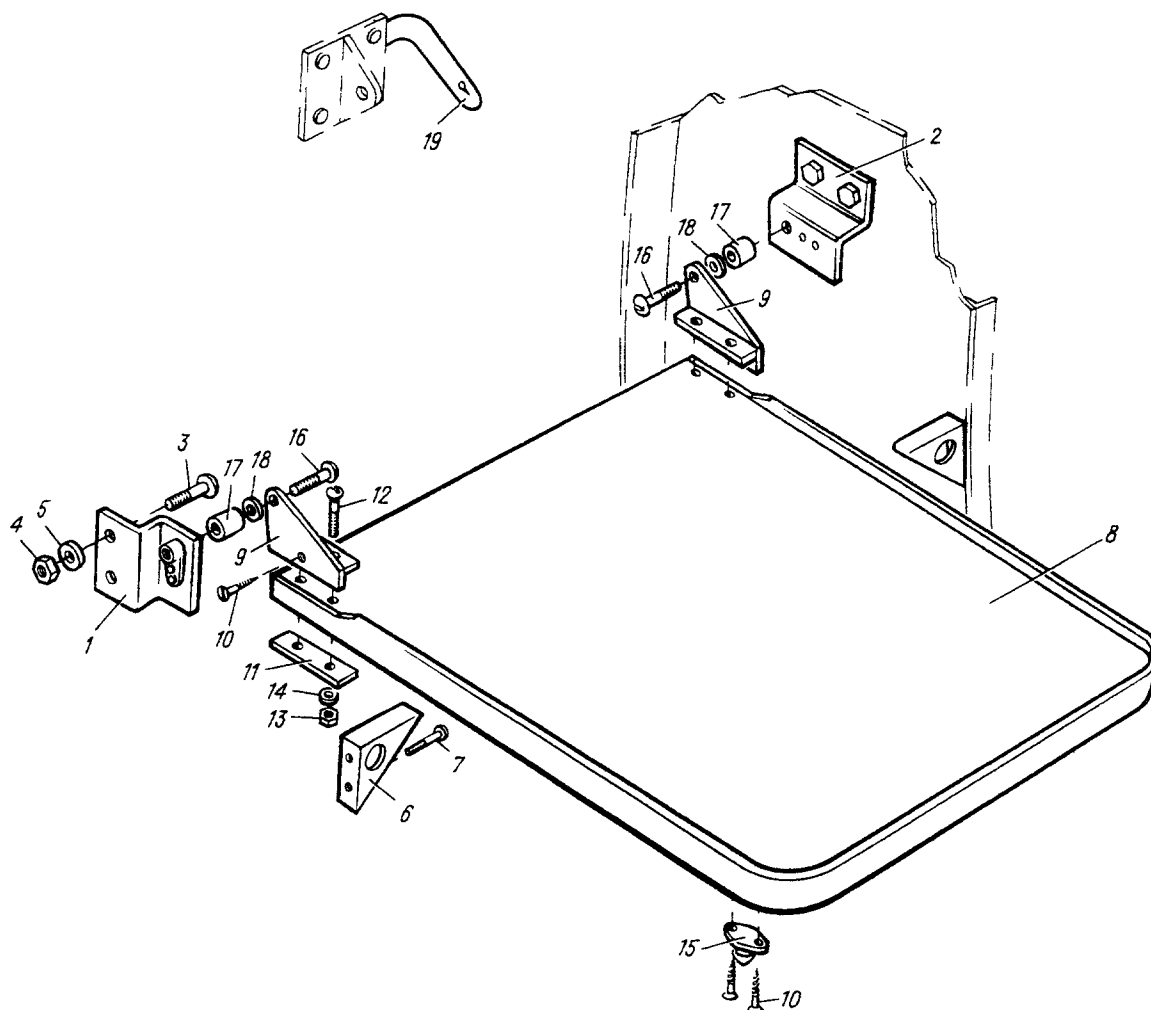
УСТАНОВКА СТОЛИКА МЕДПРАБОТНИКА
